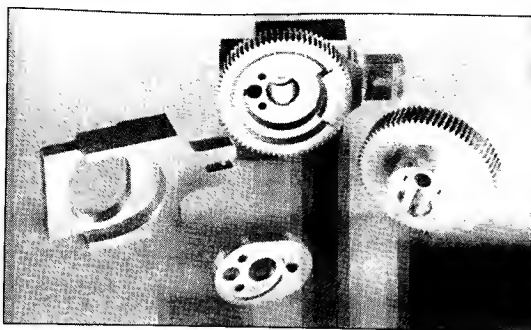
Кривошипное устройство, противовес и эксцентрическая шестерня механического лобзика
